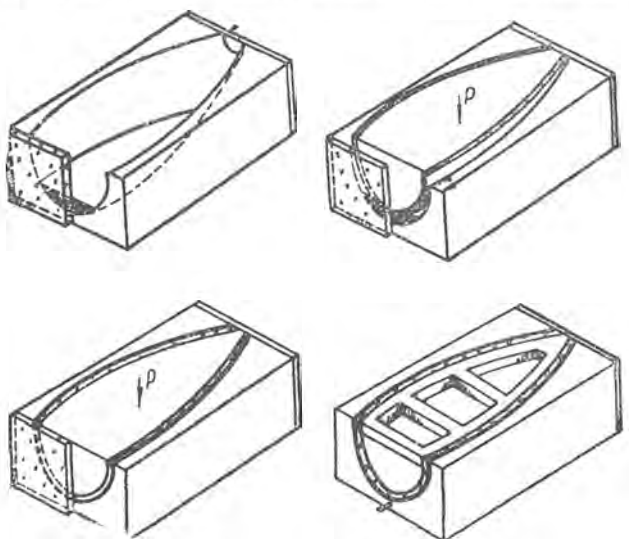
Схема получения и применения облицовочного пластика в виде листовой заготовки:
